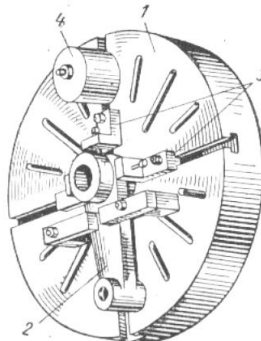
Установка и закрепление шатуна на планшайбе 1-планшайба (чугунный диск); 2-шатун(закрепляемая деталь); 3-крепёжные угольники с болтами; 4-груз-противовес.
